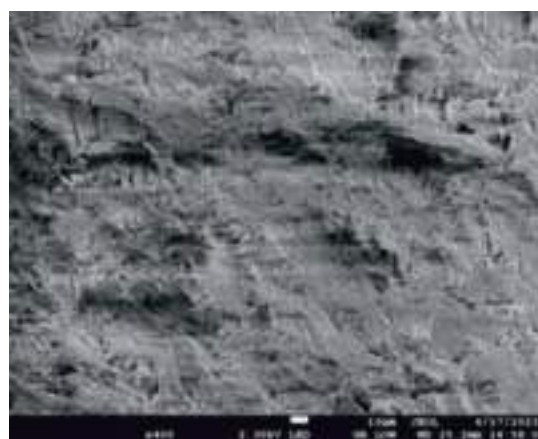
Цилиндрическая поверхность ПНБ после токарной обработки (микроскоп электронный JEOL JSM-7100F. $\times 400$). Шероховатость R_a 1,25...1,6
